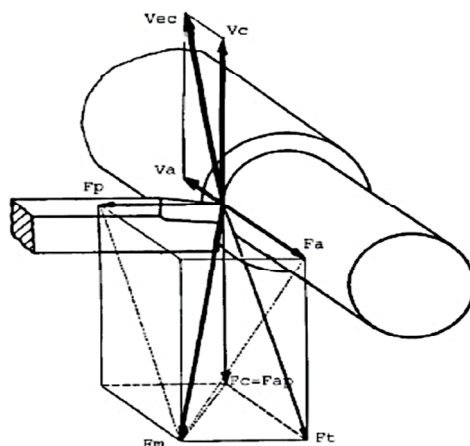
Componentes da força de maquinagem no torneamento cilíndrico [3].
